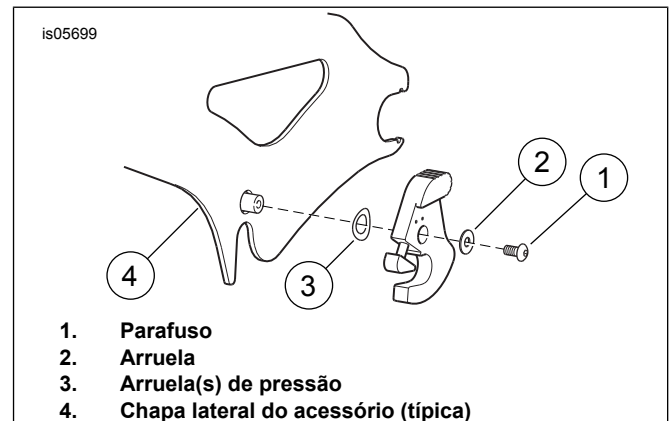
Remova a dobradiça (instalação esquerda externa exibida)
